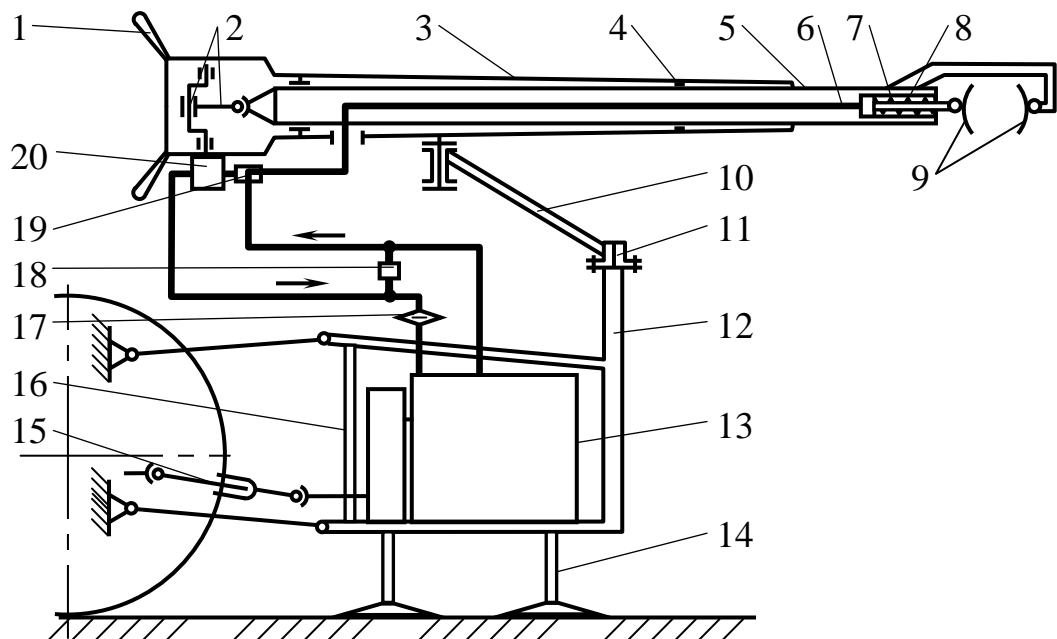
Схема турельного струшувача ТФГ плодозбиральної машини (Угорщина): 1 – рукоятки; 2 – кривошипно-повзунний механізм; 3 – корпус струшувача; 4 – підшипники ковзання; 5 – вібруючий шток; 6 – маслопровід; 7 – гідроциліндр; 8 – пружина; 9 – затискні губки; 10 – похила балка; 11 – упорний підшипник; 12 – стійка; 13 – насосна станція; 14 – башмаки; 15 – карданний вал; 16 – рама; 17 – масляний фільтр; 18 – запобіжний клапан; 19 – клапан тиску; 20 – гідродвигун
